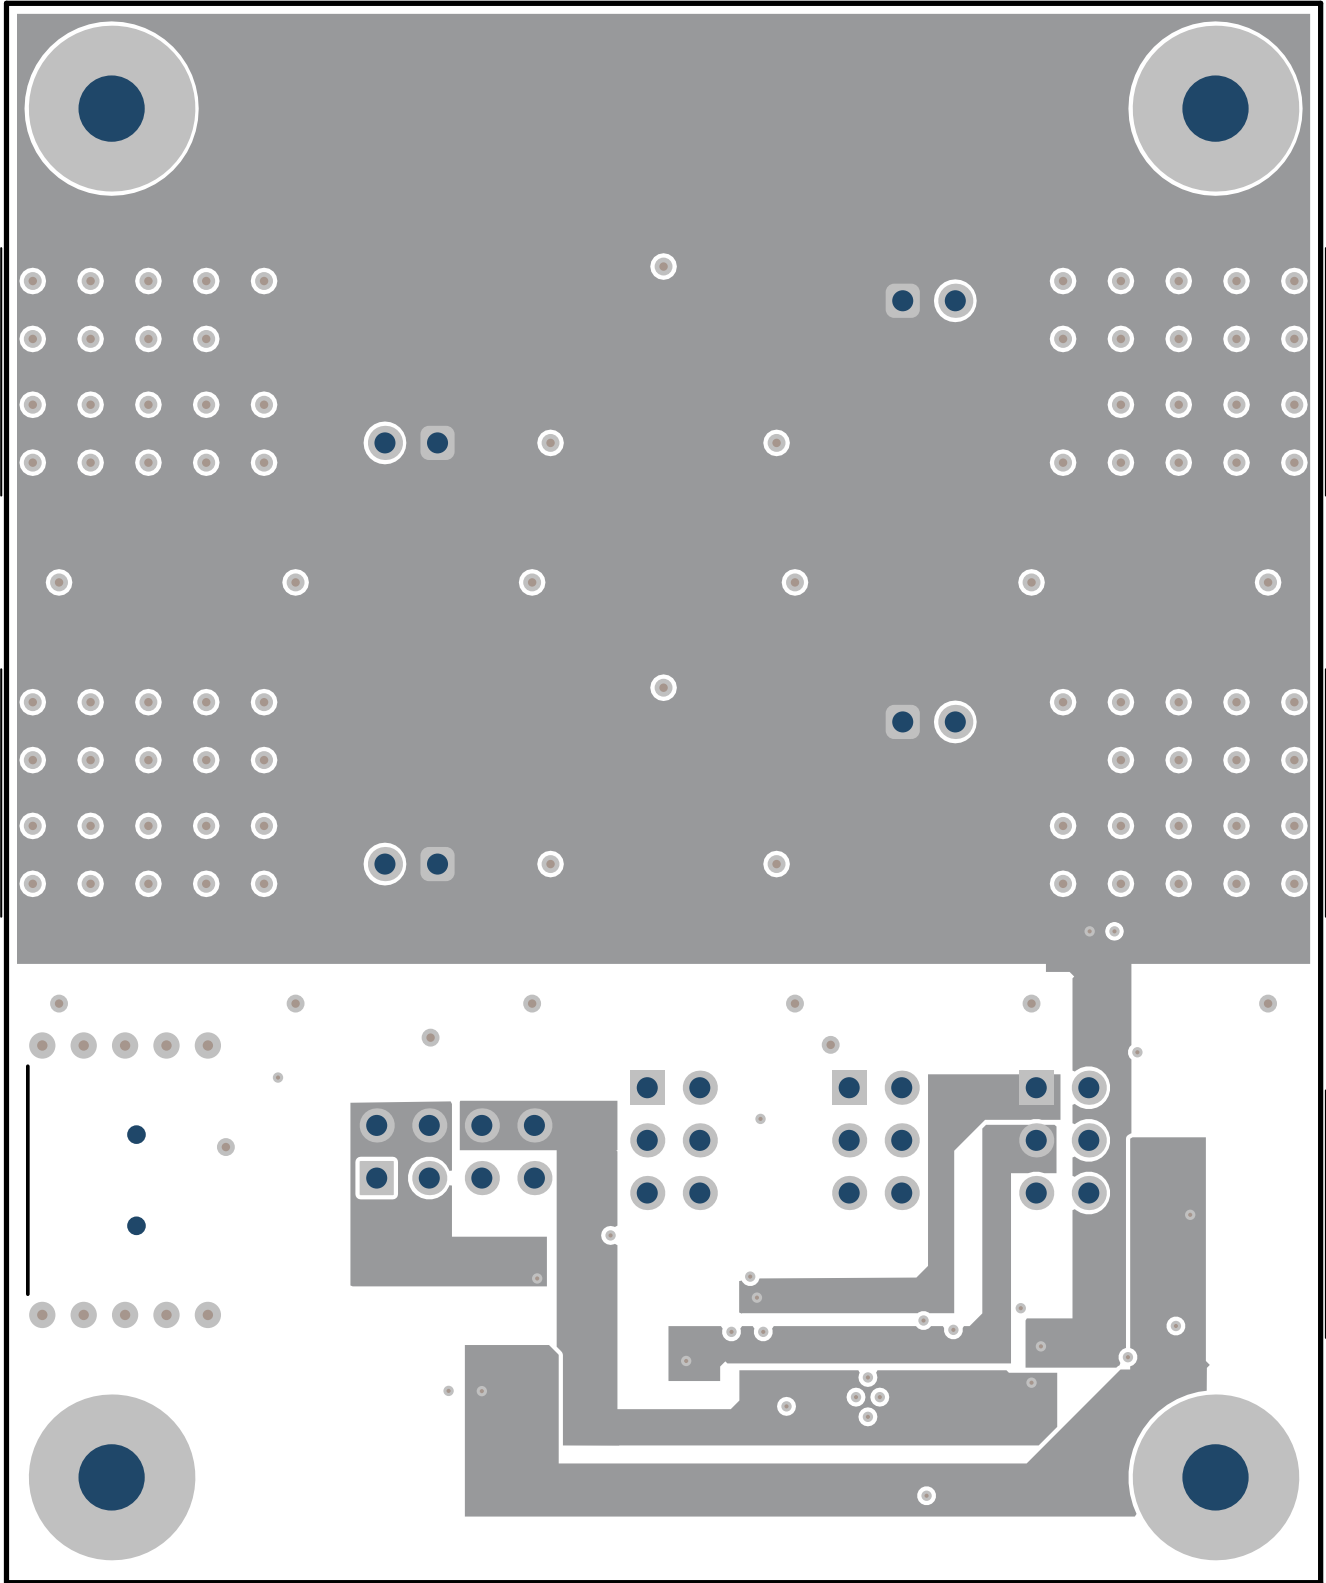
CDC6 EVM 的 PCB 布局示例 - 电源层
